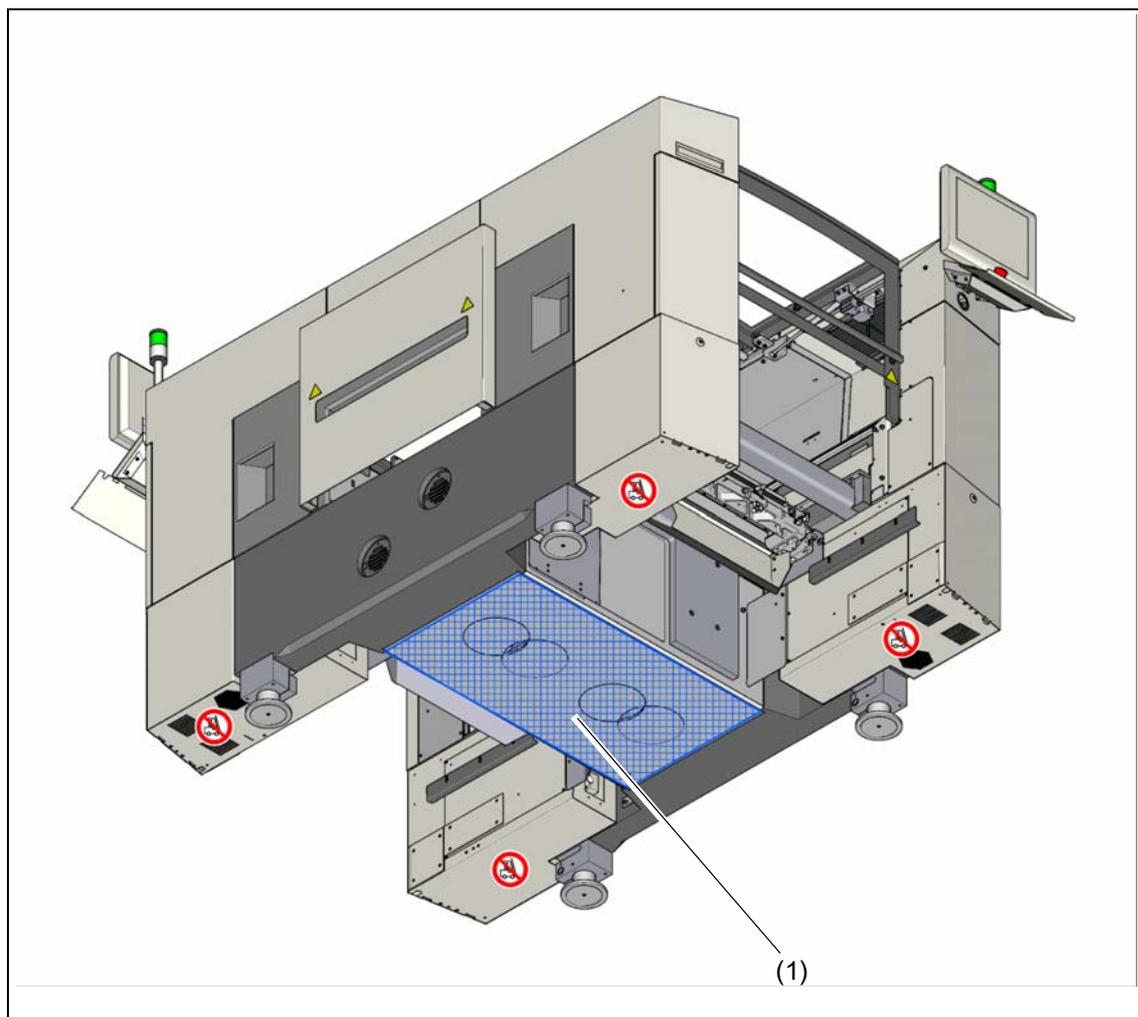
3 接触表面 - 货叉与 PCB 传送方向平行
